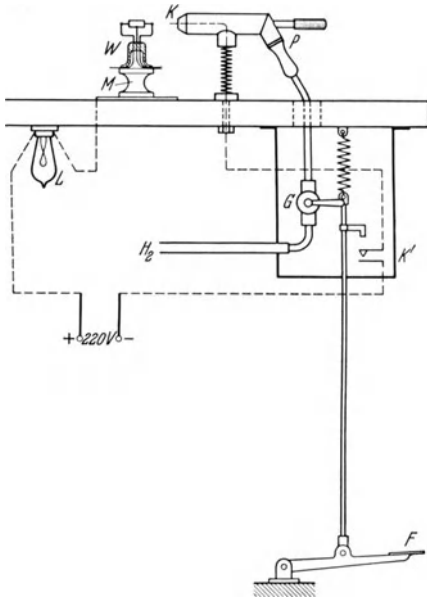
Vorrichtung zum Schweißen im H₂-Strom mittels Gleichstromlichtbogen zwischen Kohlelektrode und Werkstück.
